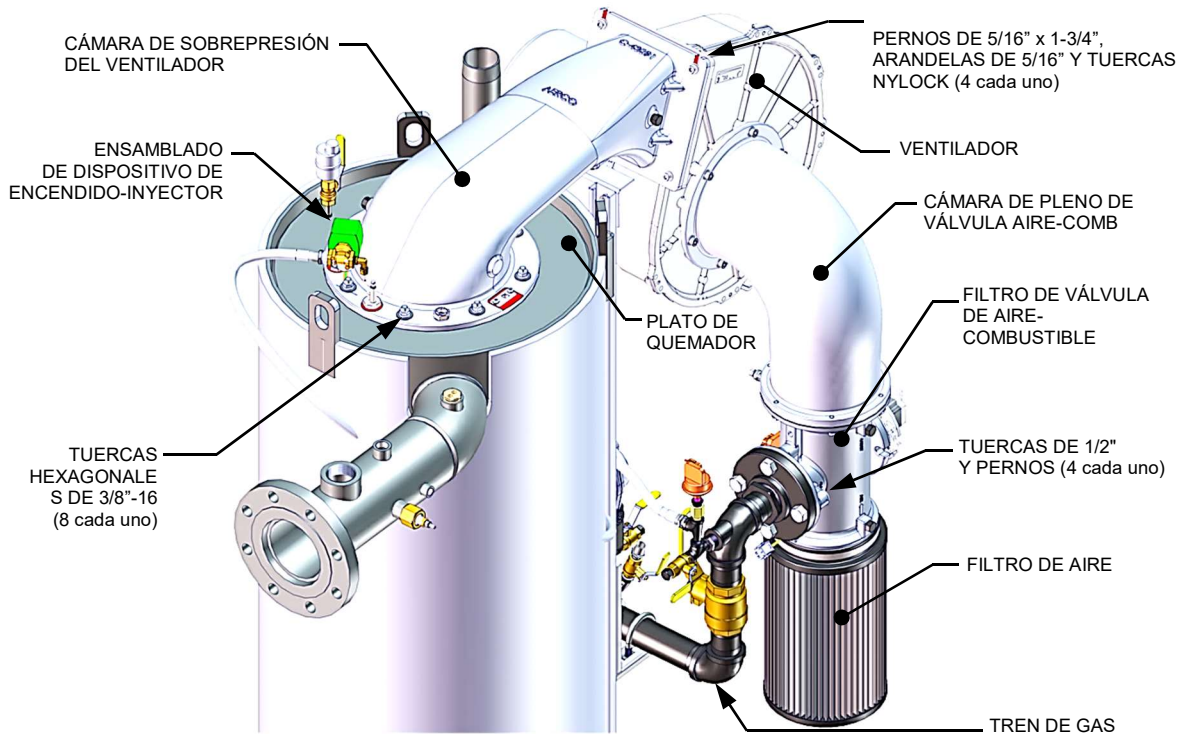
Información de montaje de ensamblado del quemador de BMK 2500/3000
